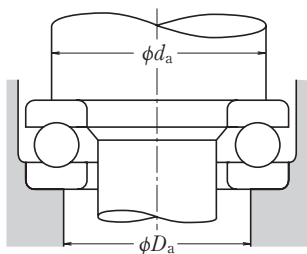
Диаметры опорной поверхности для упорных шарикоподшипников
